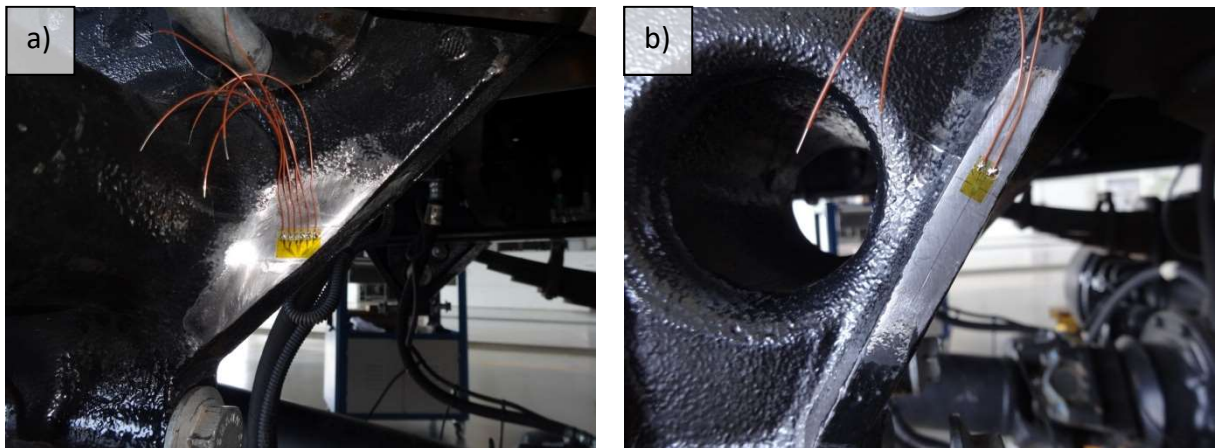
Fotos do suporte dianteiro esquerdo – vista geral
